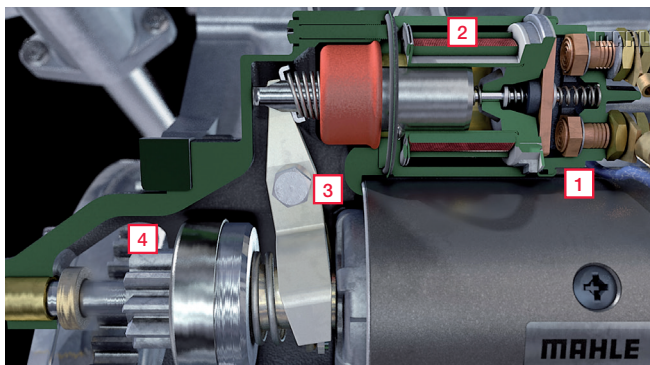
Sección del motor de arranque con puente de contacto (1) solenoide (2), palanca de embrague (3) y piñón libre (4)
